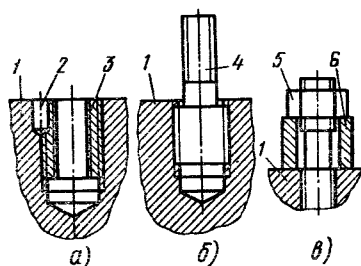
Восстановление резьбовых соединений установкой футорки (а), ступенчатой шпильки (б), шпильки на клею (в)
